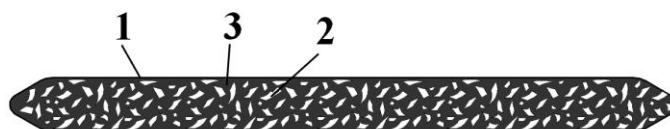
Конструкция расходного электрода: 1 – оболочка (алюминиевая фольга); 2 – титановая стружка; 3 – порошок кремния
